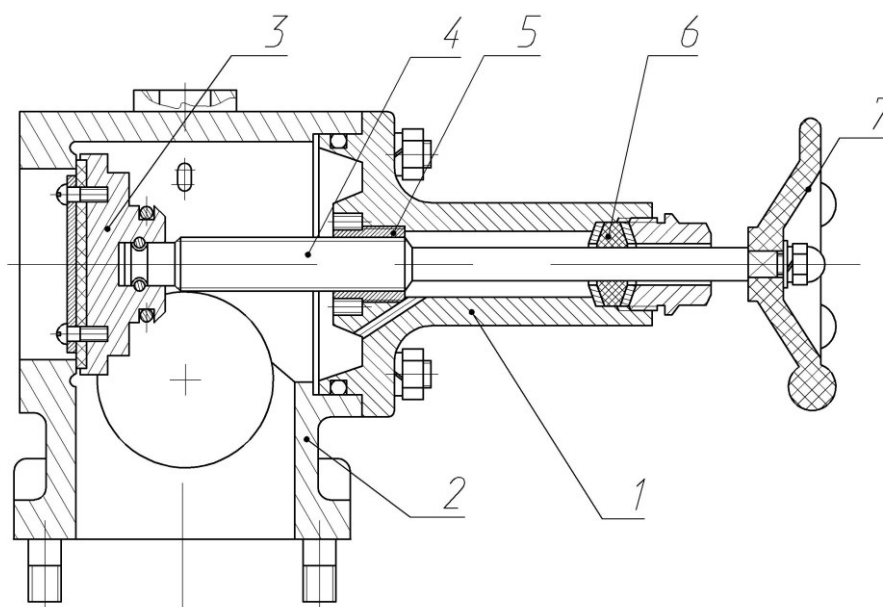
Коллектор (продольный разрез по оси задвижки «В цистерну»): 1 – корпус задвижки; 2 – коллектор; 3 – клапан; 4 – шпиндель; 5 – втулка; 6 – уплотнение; 7 - маховик.
